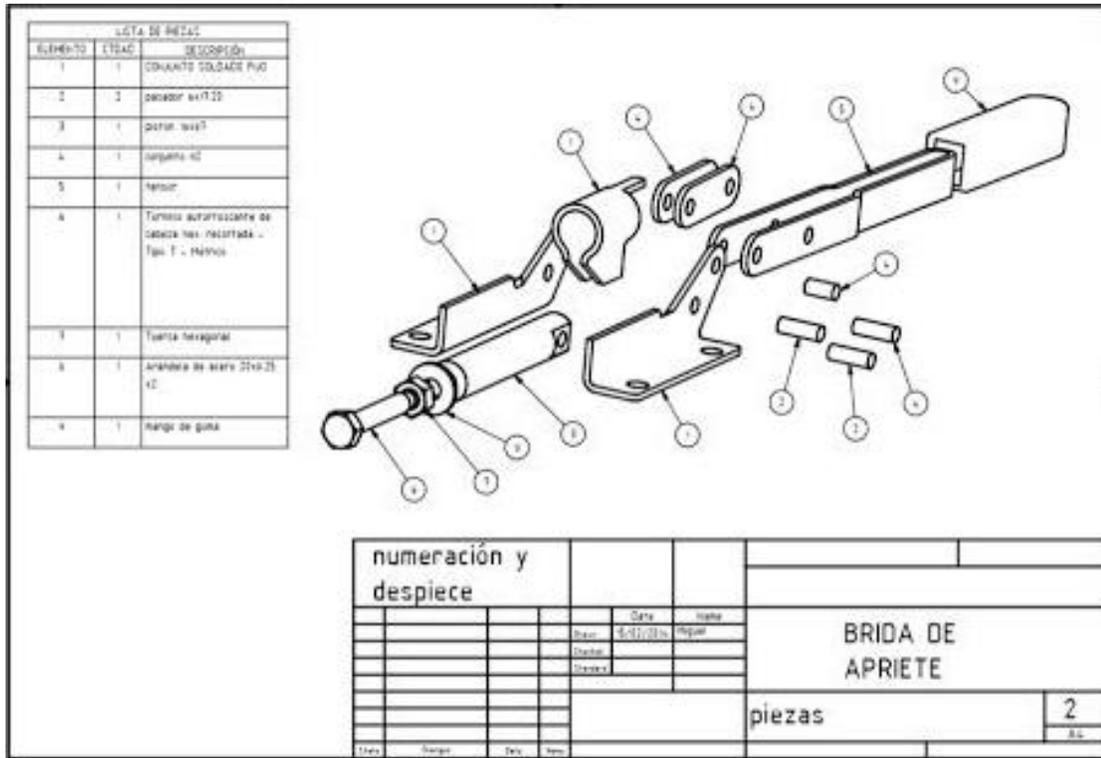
Plano de despiece (Fuente: Impresión de pantalla youtube.com)
